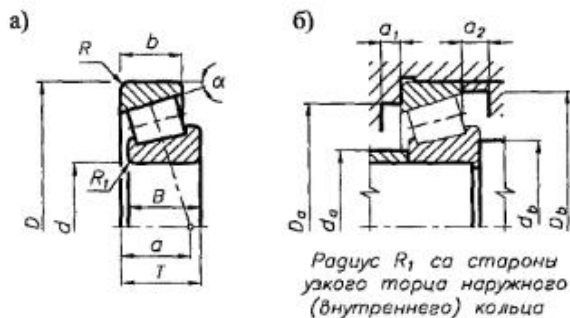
Габаритные и установочные размеры роликовых конических однорядных подшипников
